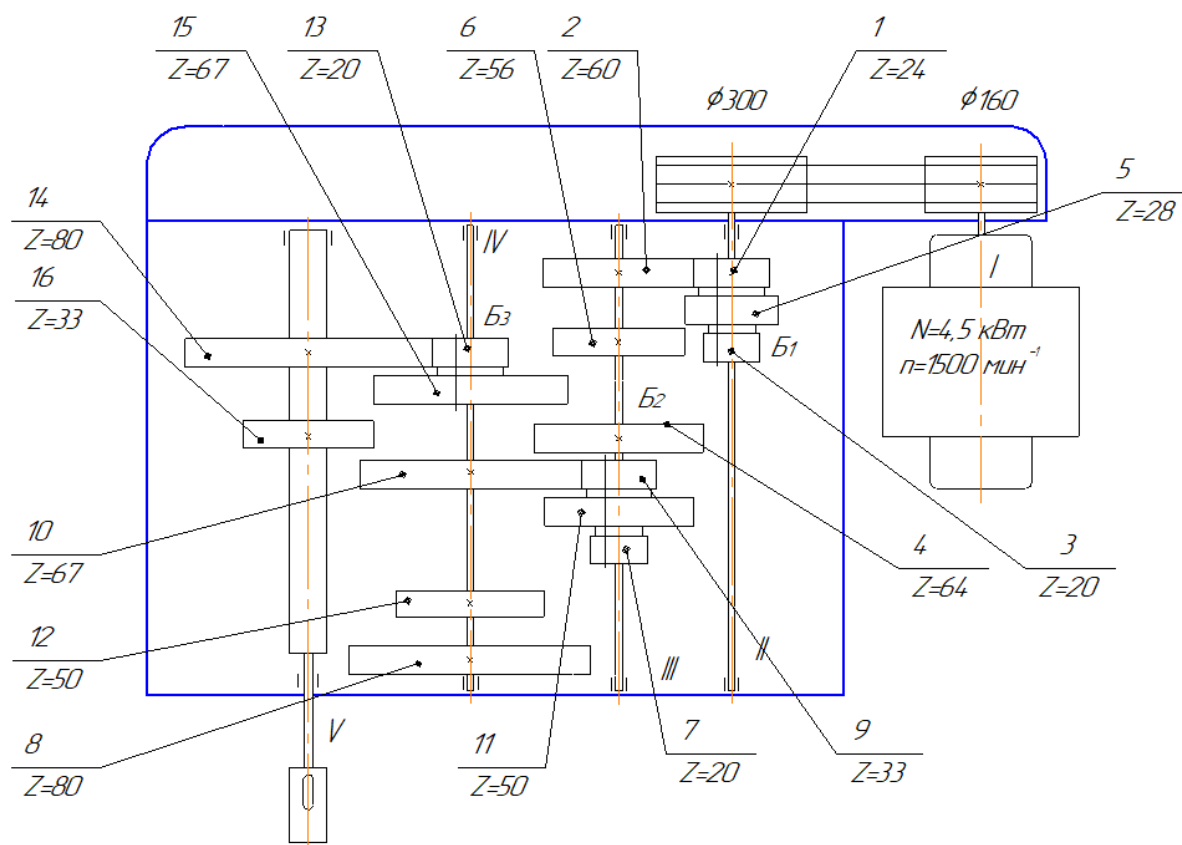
Кинематическая схема коробки скоростей модернизированного станка
